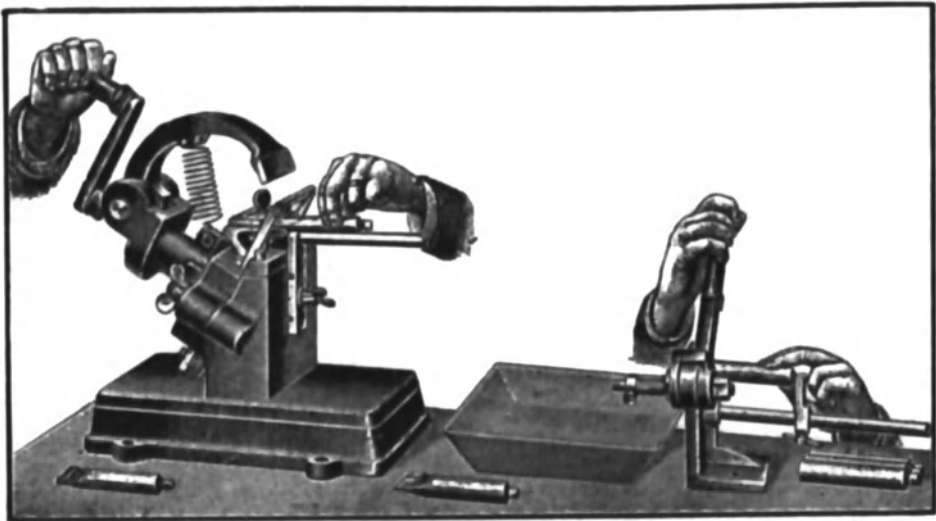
Tubenverschleißmaschine für Handbetrieb.
